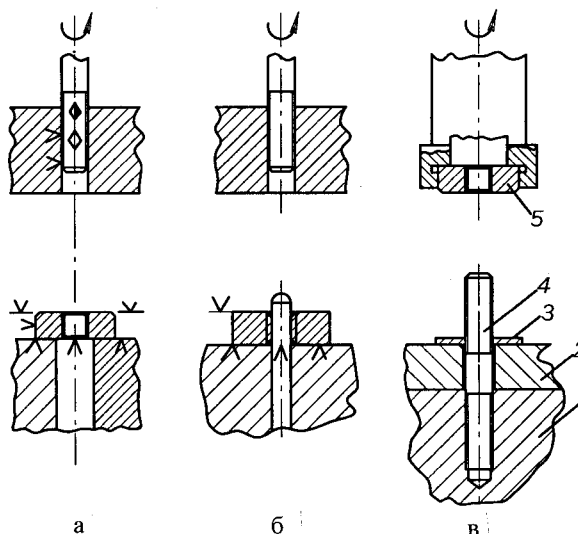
Схеми базування різьбових з'єднань: 1 - корпус, 2 - кришка, 3 - шайба, 4 - шпилька, 5 - гайка
